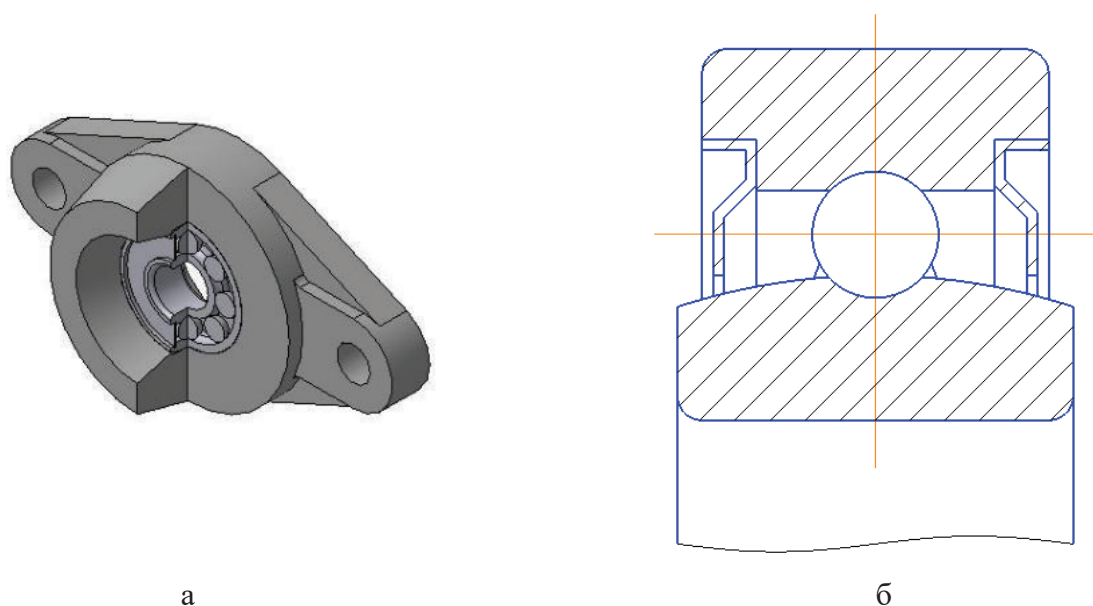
Разрез 3d модели подшипника (а), чертежа подшипника в разрезе (б)
